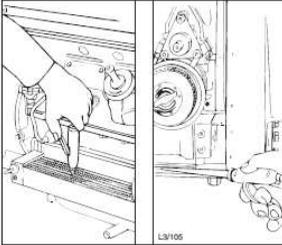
Reinigung des Ölkühlers und des Motorblocks
